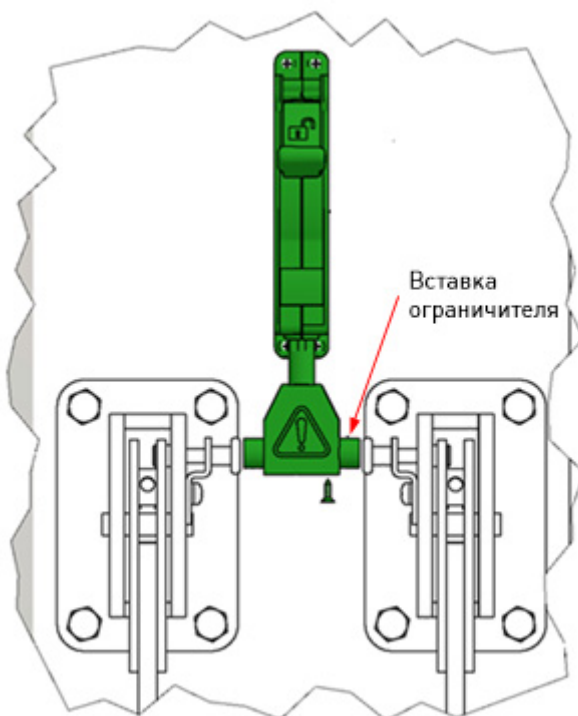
Установка блокиратора со сдвоенными разъединителями
